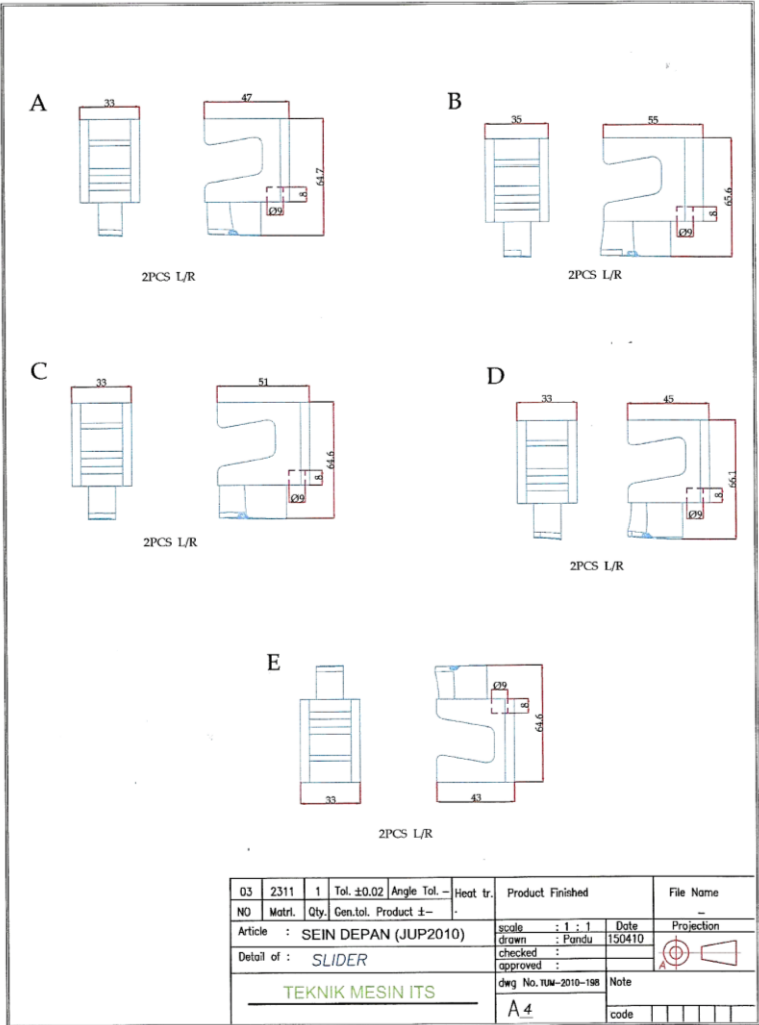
Detail *drawing* 2D komponen untuk *insert core
